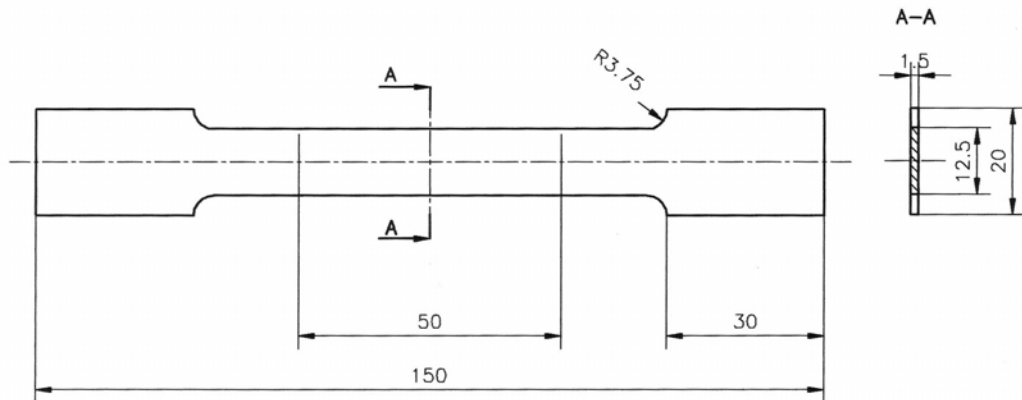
Geometria e dimensões do provete para ensaio de tracção.
